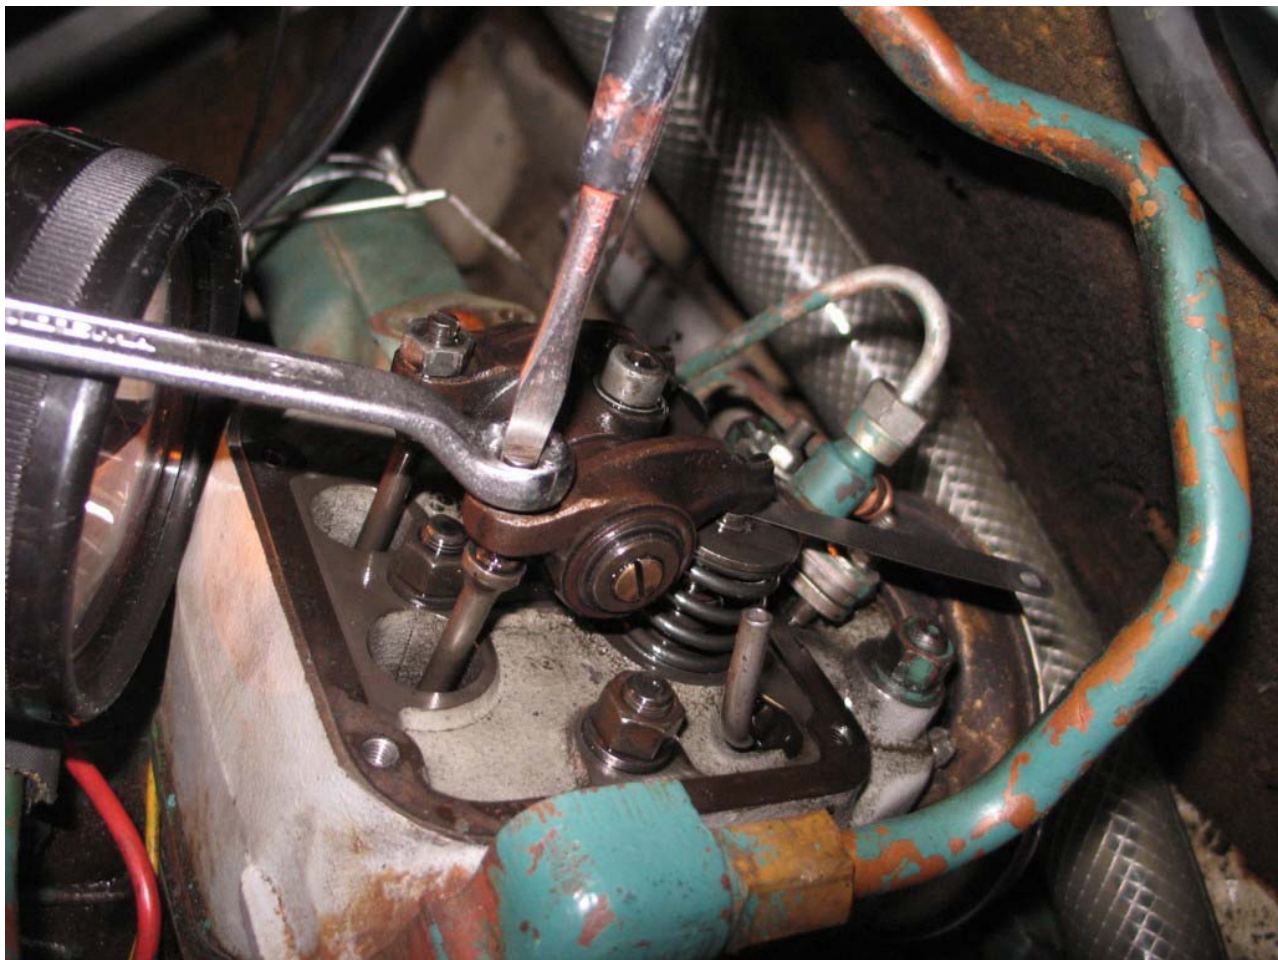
Ventiljustering. Jag brukar använda 13mm ringnyckel, skruvmejsel och bladmått. På bilden är det insugningsventilen som justeras till 0,3 mm, bladmåttet sitter på plats.
